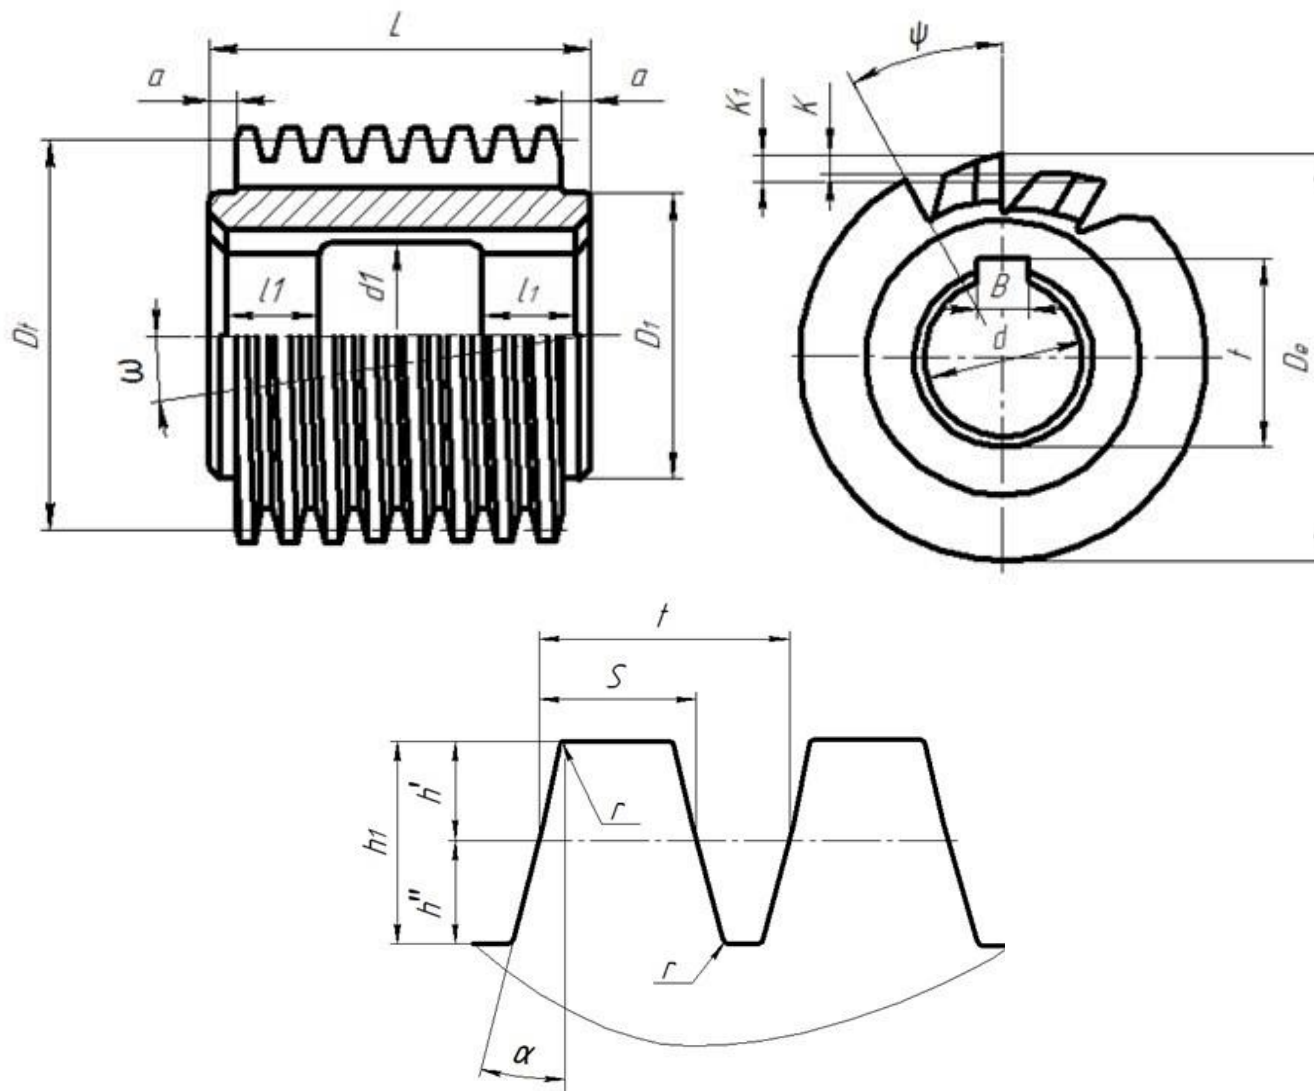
Ескіз черв'ячної зуборізної фрези
